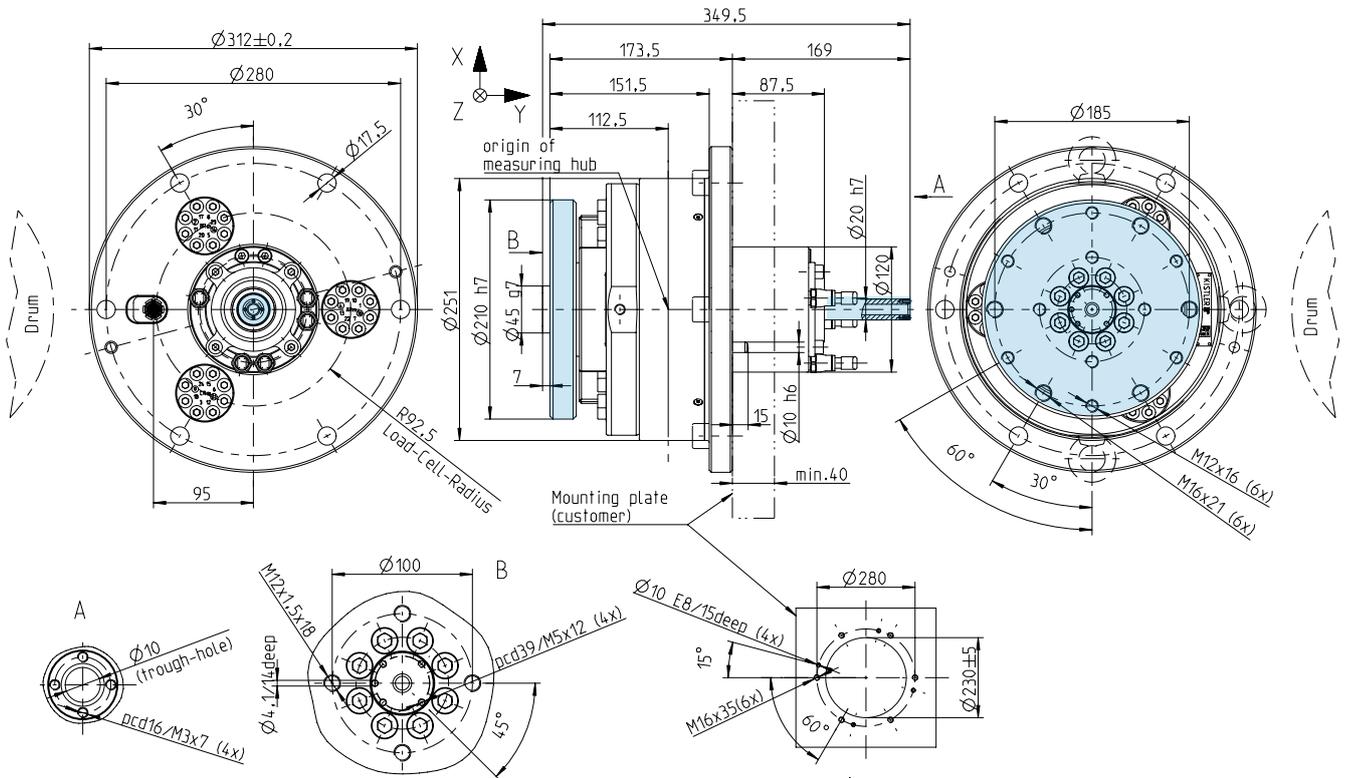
Übersichtszeichnung RoaDyn S220; rotierende Teile sind blau eingefärbt
